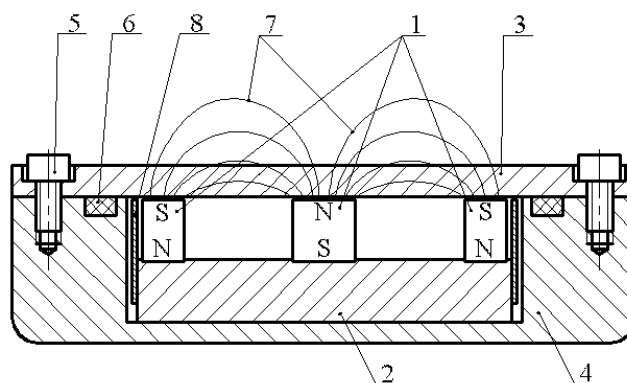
Поперечный разрез магнетрона: 1-магниты; 2-магнитопровод; 3- мишень; 4-корпус; 5-винты крепления мишени; 6- резиновое уплотнение; 7-силовые линии магнитного поля; 8-магнитный шунт.
